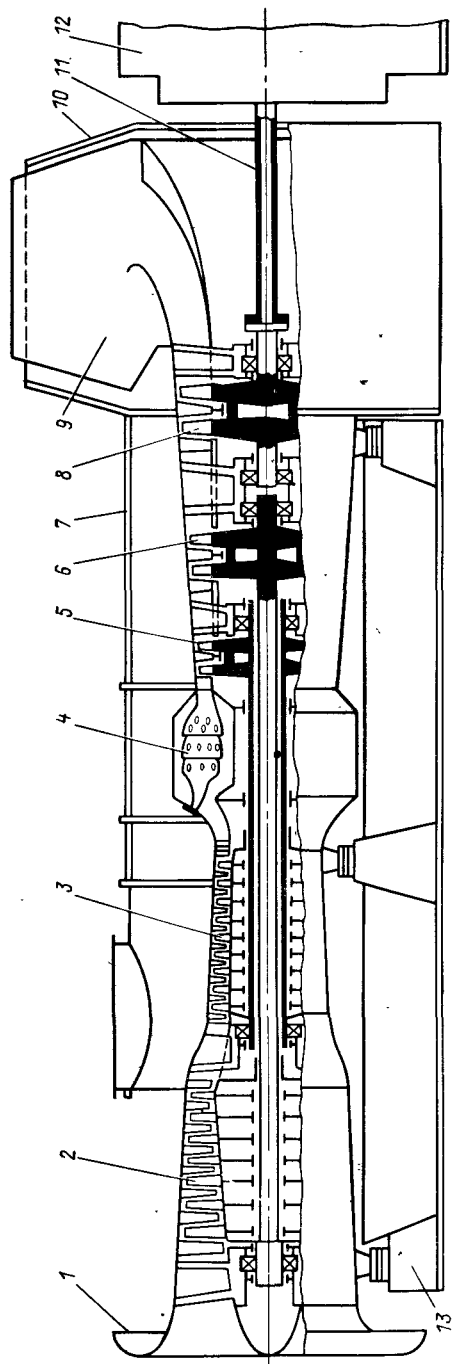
Схема судового ГТД прямоточного типа с двухкаскадным компрессором
